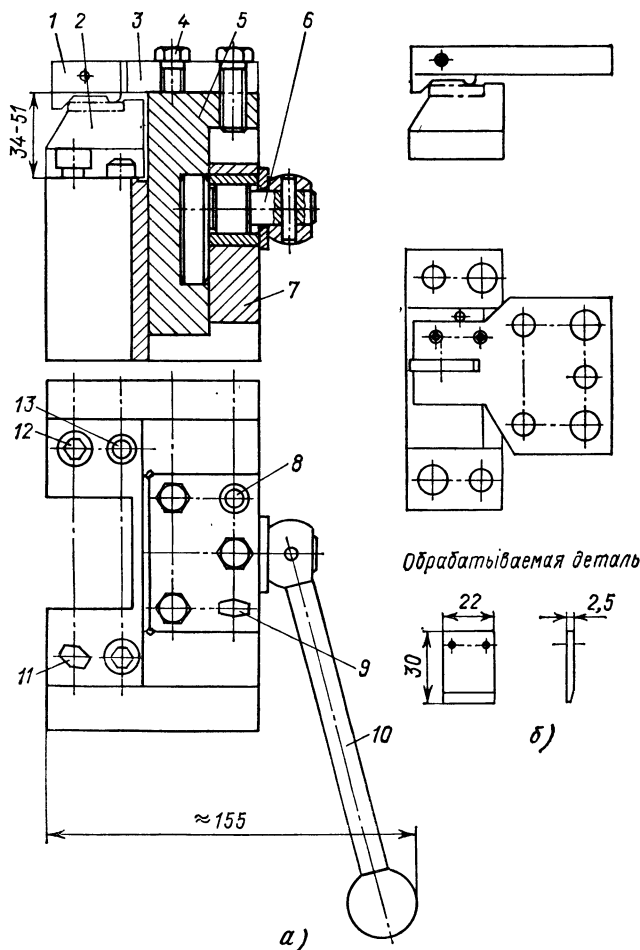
Перенастраиваемый кондуктор для сверления отверстий в коротких планках, сухарях, кулачках и шпонках
